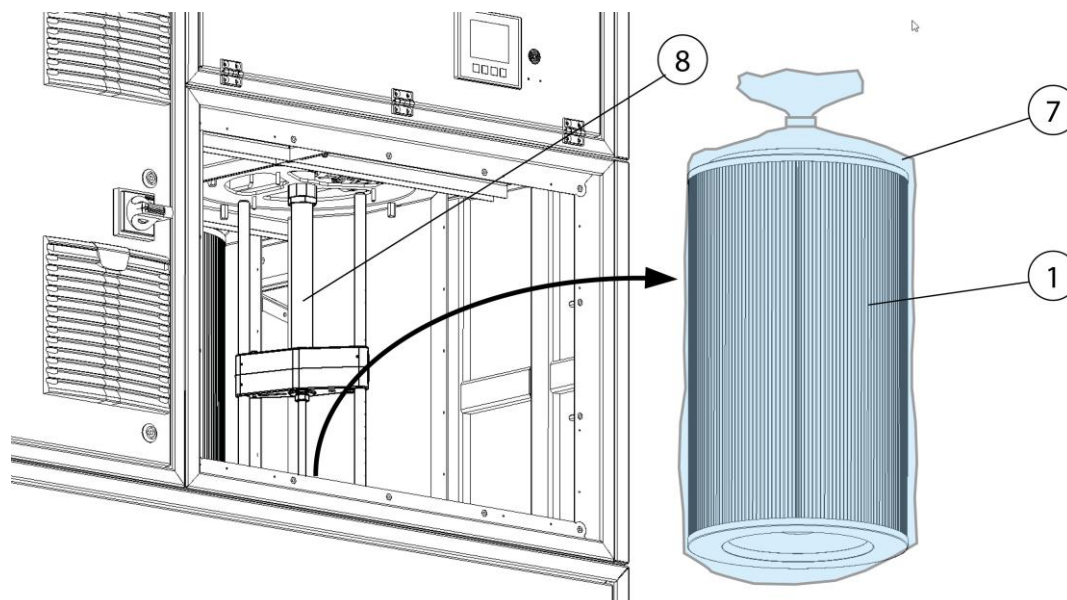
Remplacement du filtre - retrait de la cartouche filtrante
